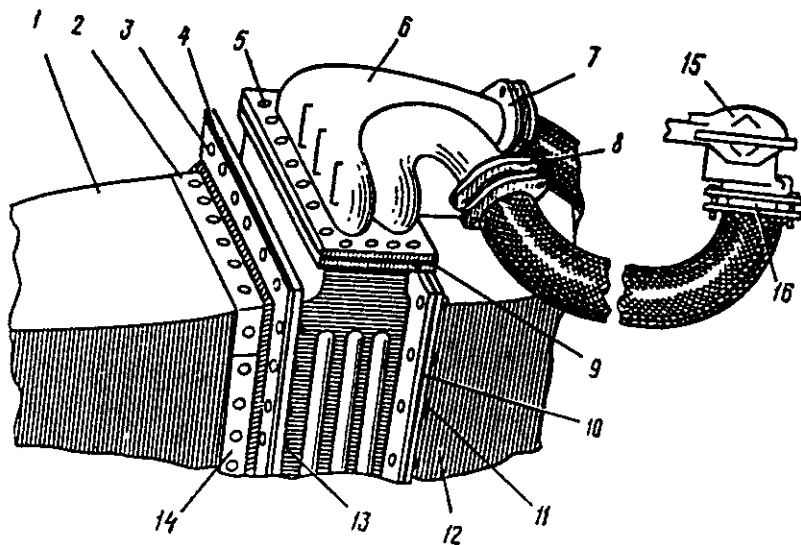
Установка воздуховоздушного радиатора (изд. 1639А):
